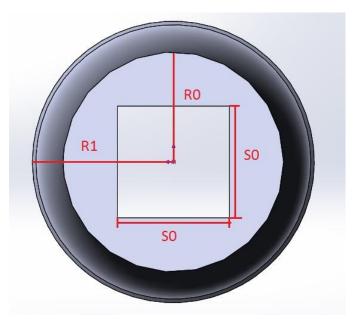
Радиус под посадочный квадрат (R0), под рабочую область (R1), размеры посадочного квадрата (S0)
